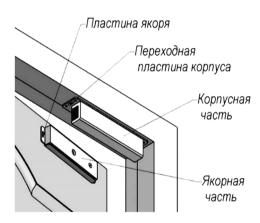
Вариант крепления корпуса замка на переходной пластине
